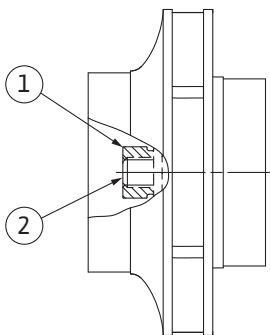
Posición correcta de la tuerca del rodete tras el montaje
